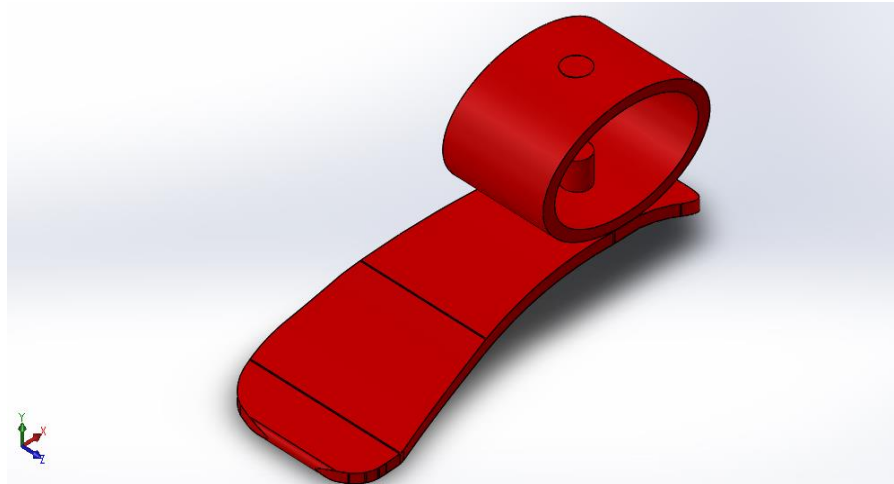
Ensamble del conjunto anillo plantilla [Autores].
